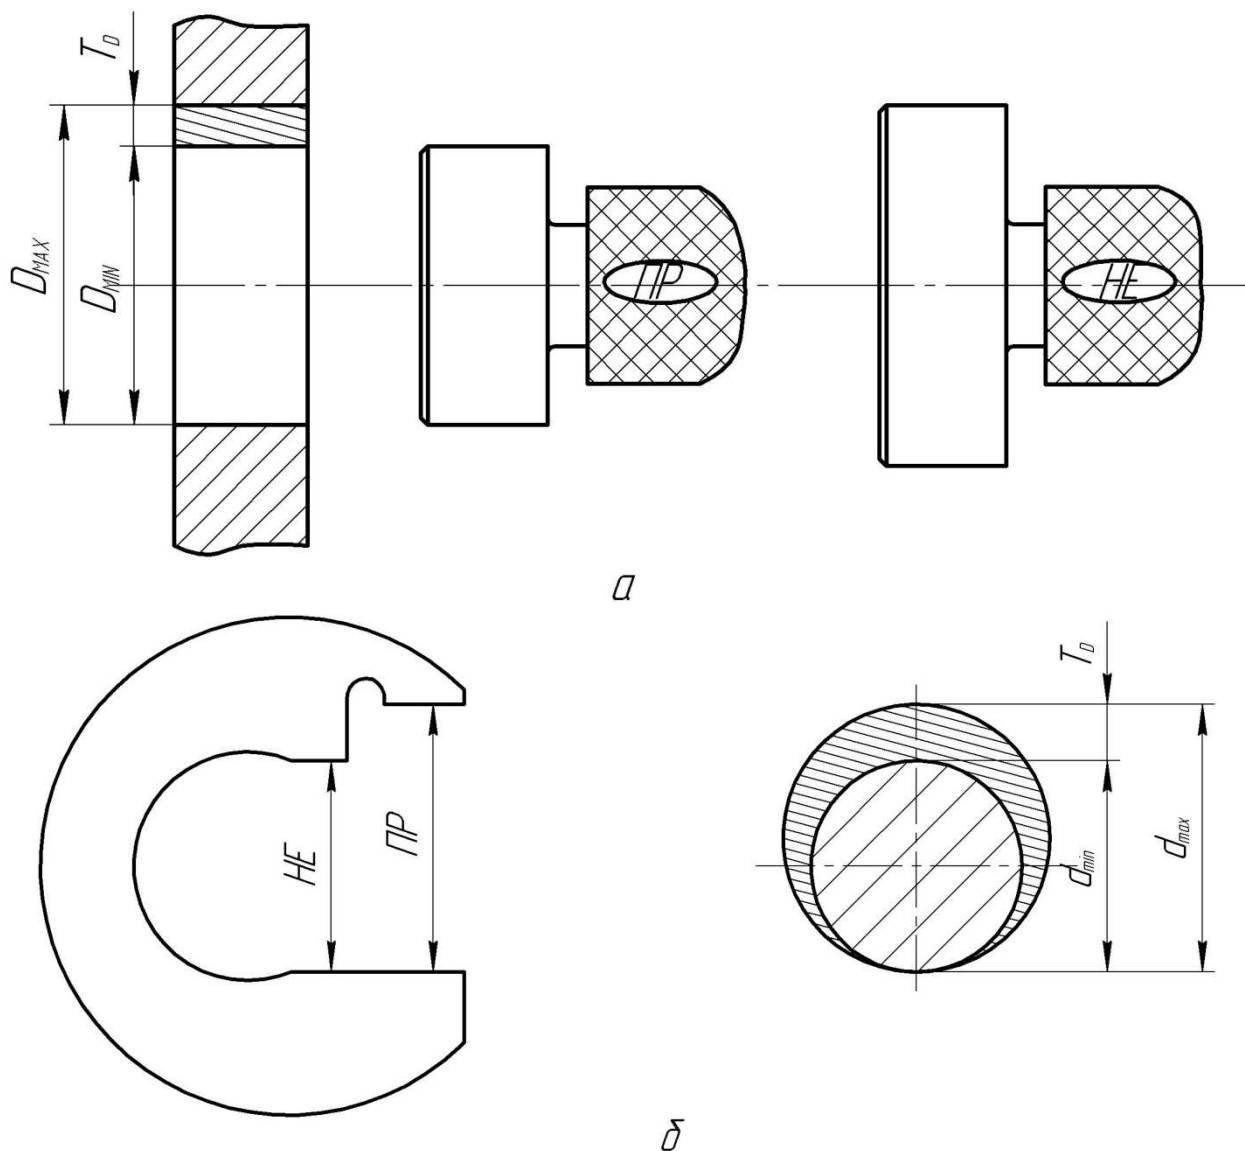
Схемы контроля гладкими предельными калибрами отверстия (а) и вала(б)
